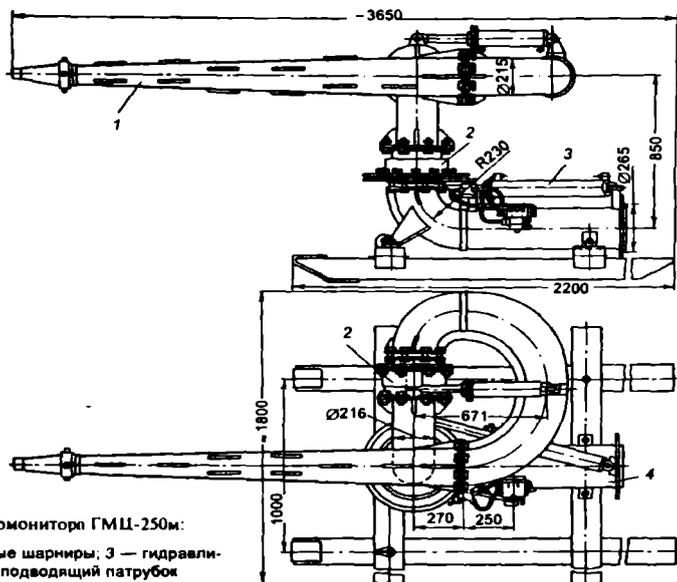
Схема гидромонитора ГМЦ-250м:
